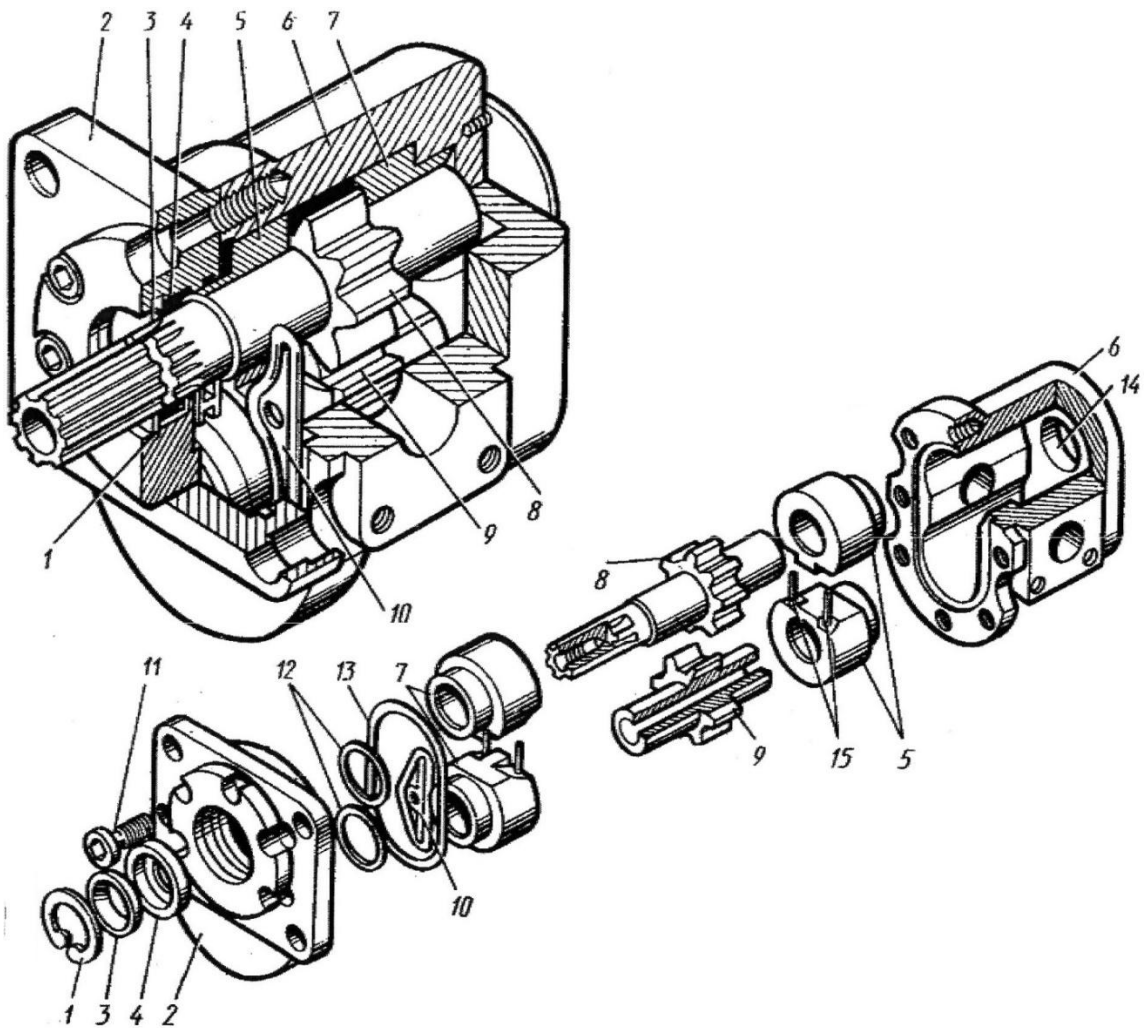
Общий вид конструкции шестеренного насоса типа НШ с разнесением схемы: 1, 3, 12, 13 – уплотнительные кольца; 2 – крышка; 4 – сальниковое уплотнение; 5, 7 – втулки для фиксации валов; 6 – корпус; 8, 9 – шестерни; 10 – разгрузочная пластина; 11 – винты; 14 – дренажное отверстие; 15 – стержни
